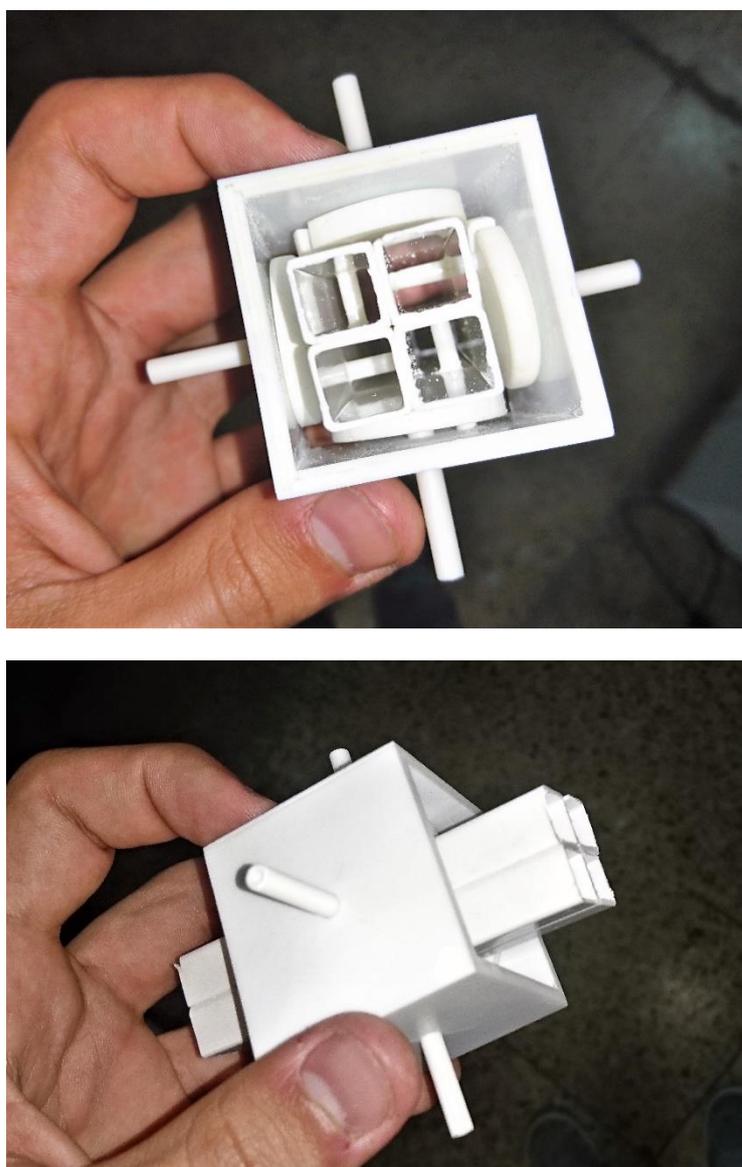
Maqueta inicial en proceso de fabricación y montaje. Fuente: Trabajo de campo.
